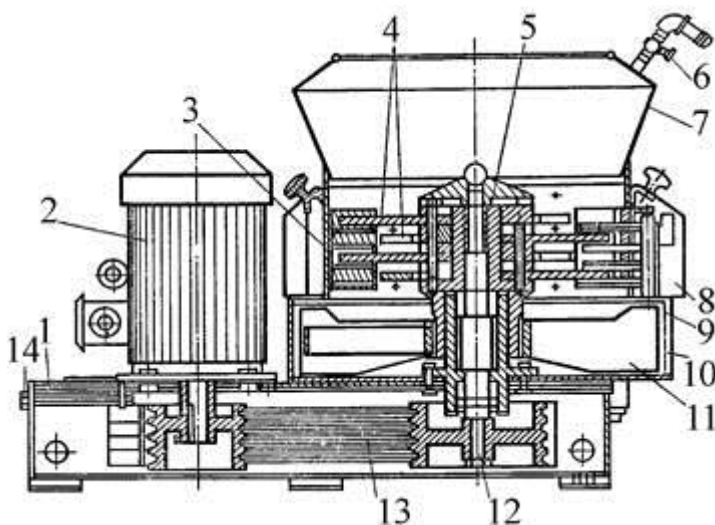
Общий вид измельчителя-смесителя кормов ИСК-3А:
